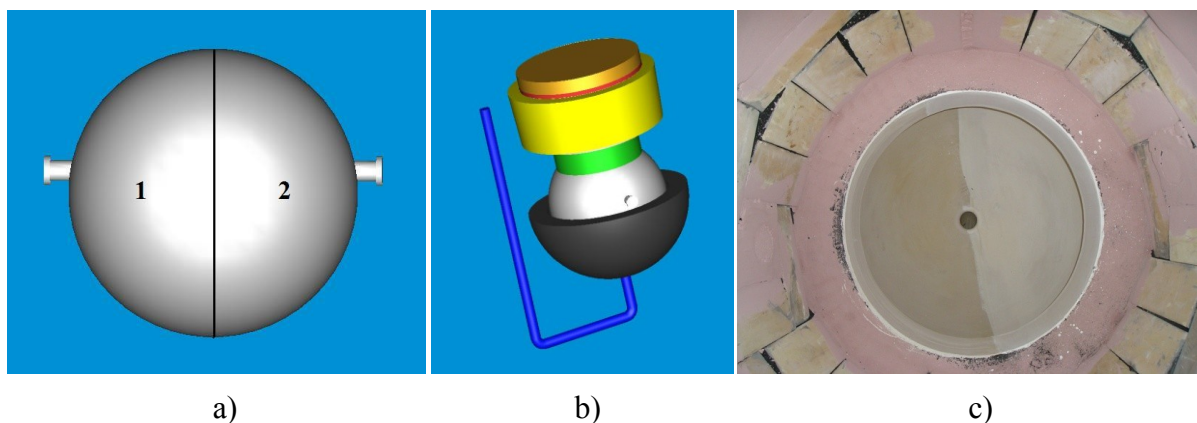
Povrch odlitku s Teno Coatingem ZBBP16
